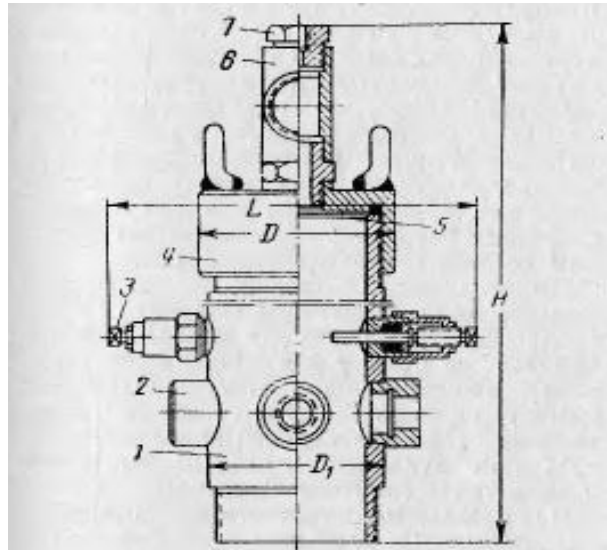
Цементувальні головки ЦГ3-120 : 1 - корпус головки; 2 – патрубок для приєднання нагнітальної лінії; 3 – стопор для пробки; 4 – кришка головки; 5 - гумова прокладка; 7 – ніпель для манометра [1]
